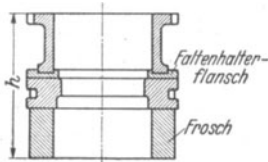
Ziehwerkzeug mit austauschbaren Einzelteilen bei festgelegter Werkzeughöhe.
